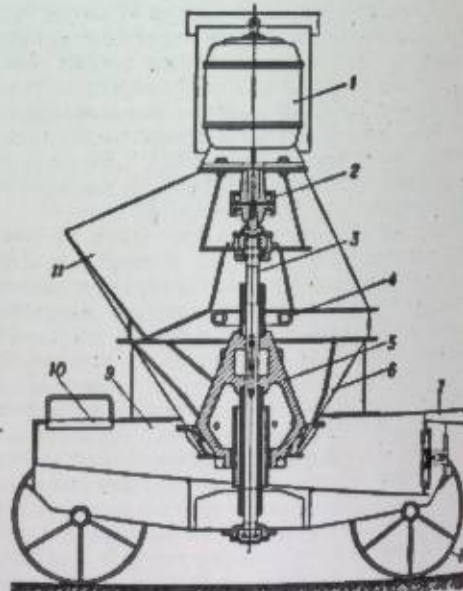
Известегасильная машина АЧ-2 фрезерного типа: 1 — фланцевый электродвигатель; 2 — упругая муфта; 3 — вертикальный вал; 4 — разбрызгиватель; 5 — ротор; 6 — рабочий конус; 7 — сливной лоток; 8 — ходовой конус; 9 — гасильный резервуар; 10 — диск; 11 — приемный бункер.
